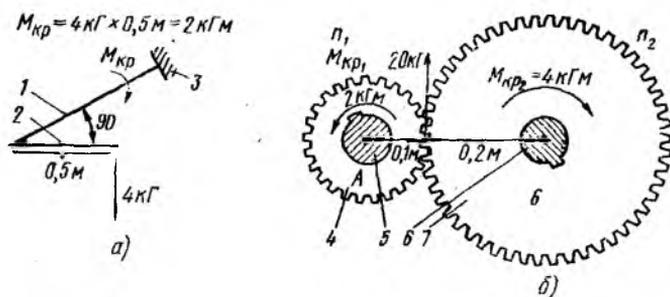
Крутящий момент на валу (а) и одноступенчатый понижающий редуктор (б):
